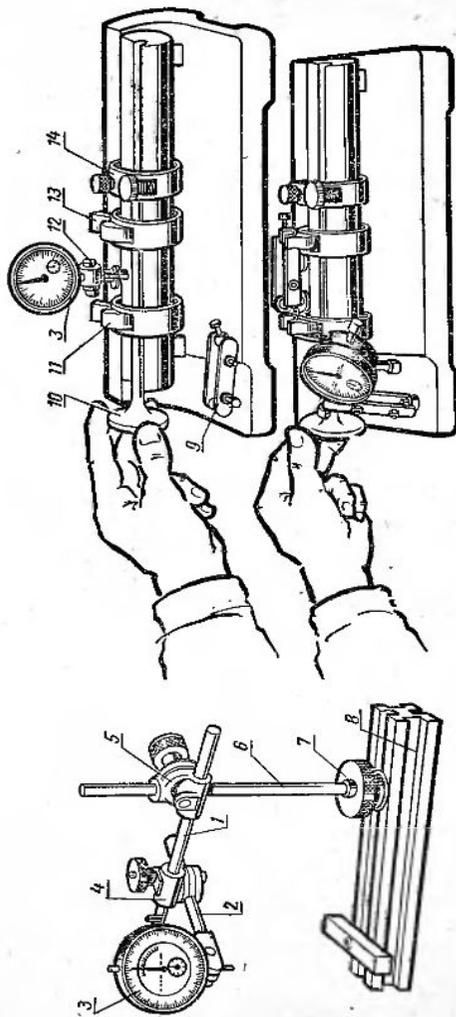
Универсальная индикаторная стойка (слева) и индикаторное приспособление (справа) для проверки плоскостей на прямолинейность стержня (верху) и боковой фаски тарелки (низу): 1, 2 и 6 — стержень; 3 — индикатор; 4 и 5 — муфты; 7 — гайка; 8 — пружина; 9 и 12 — стойки для индикатора; 10 — наконечник; 11 и 13 — пружины; 14 — упор.
